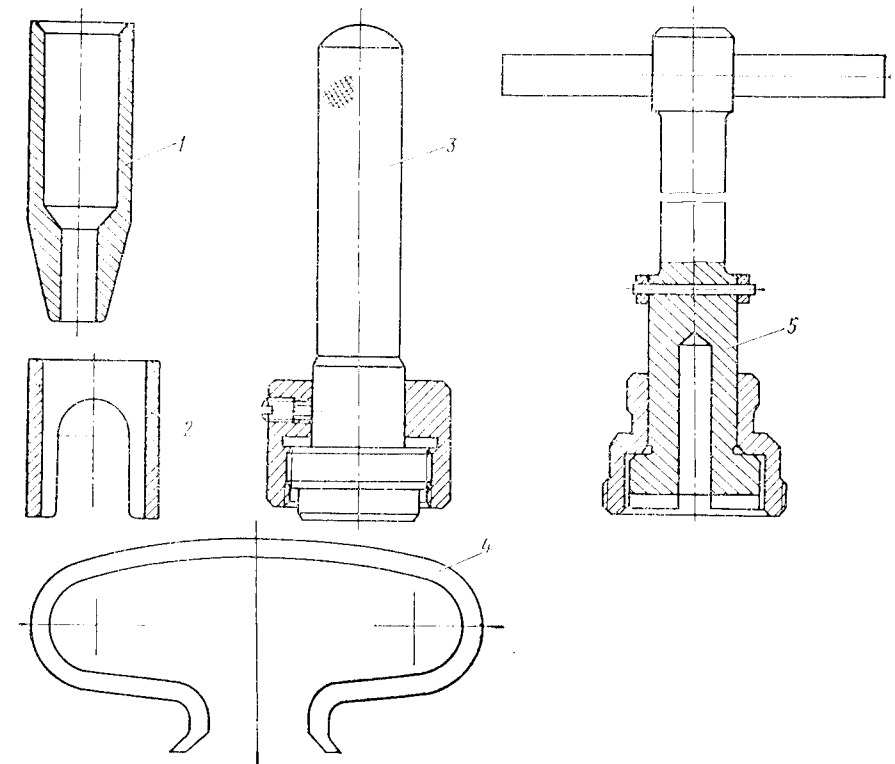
Приспособления для сборки узлов воздухораспределителя KEA.
